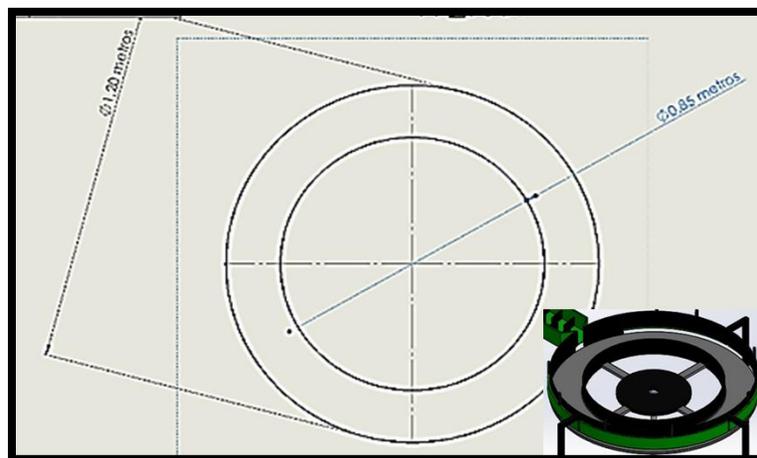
Dimensiones De La Vista Superior De La Mesa Giratoria.
